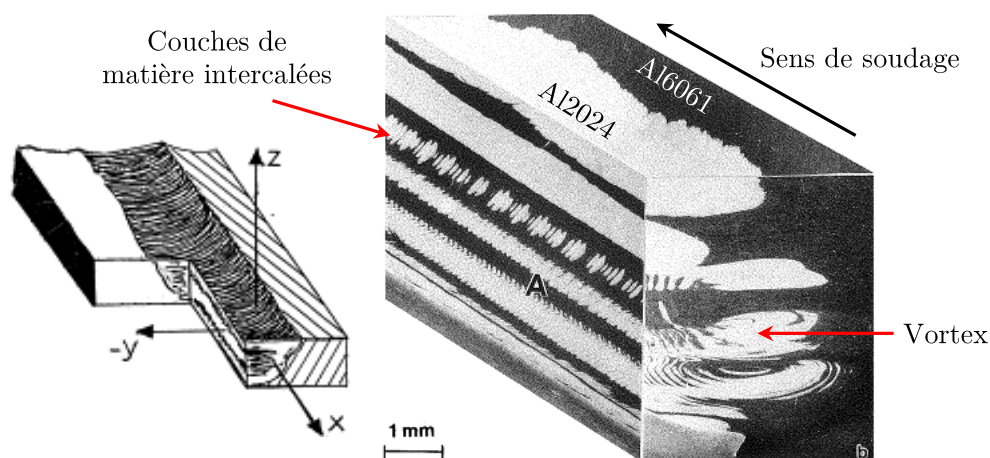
Visualisation au microscope optique du flux de matière après soudage des alliages d'aluminium Al2024/Al6061 [Li+1999].
